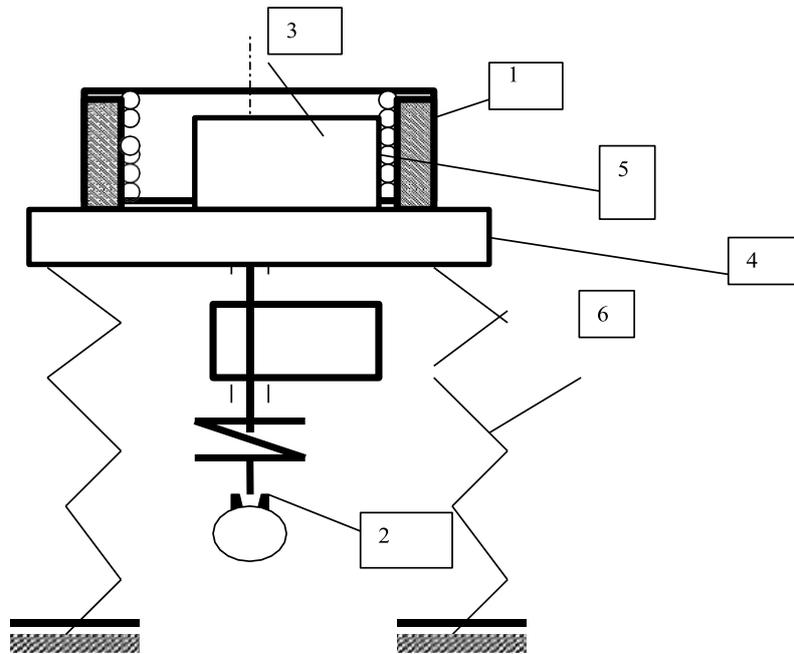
Схема обробки деталей на вібраційній машині з вертикальною віссю обертання деталі
